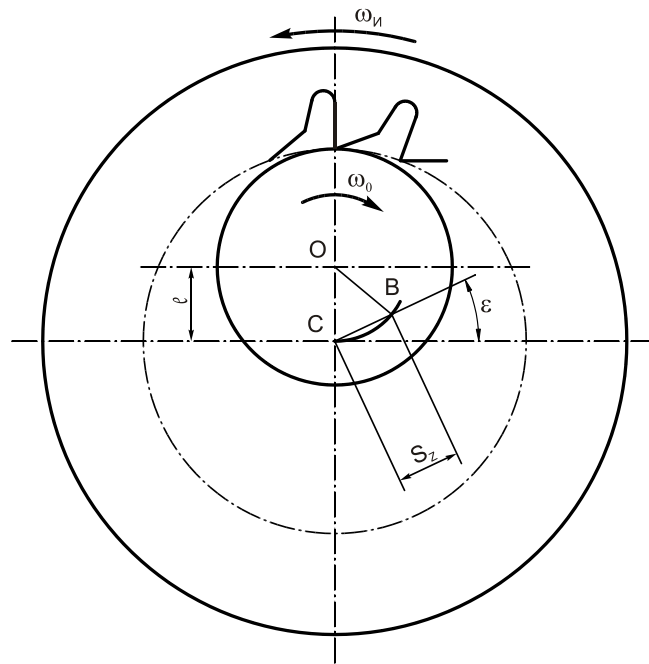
Схема охватывающего фрезерования поверхностей вращения
